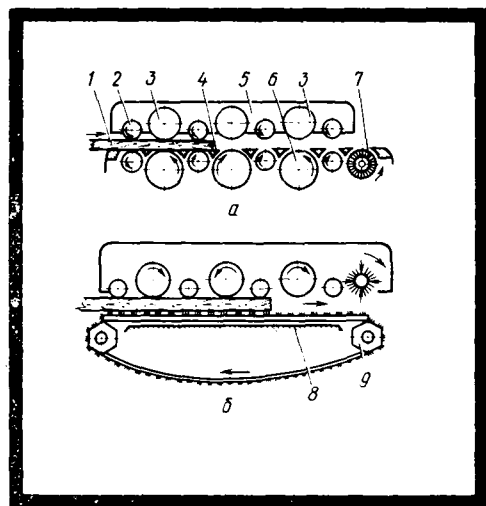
Трехцилиндровый шлифовальный станок с механической подачей:
